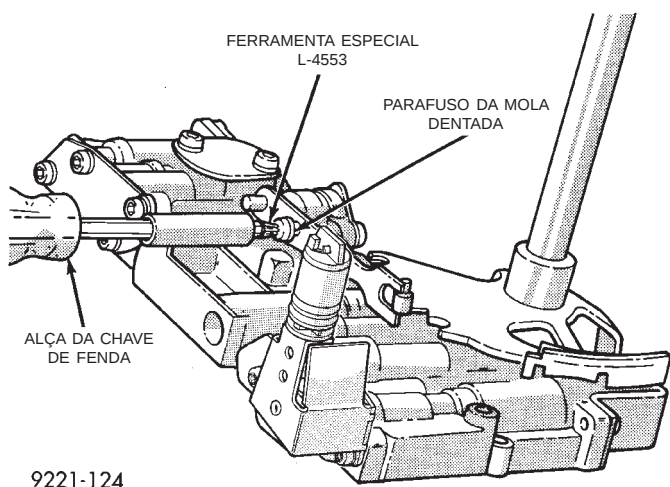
Parafuso e Mola de Fixação da Mola Dentada
